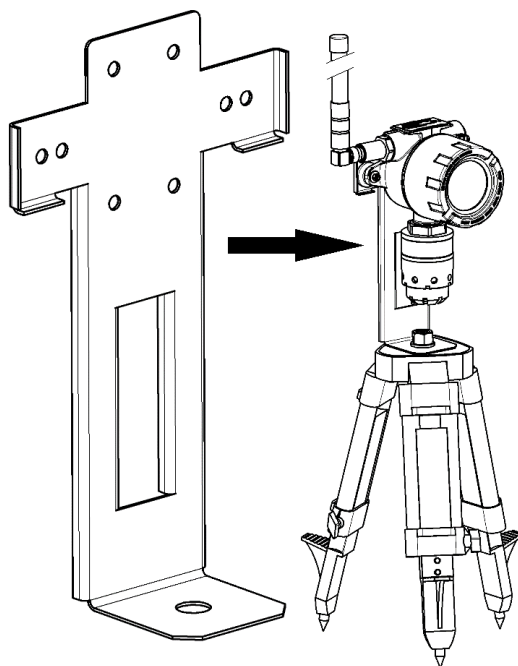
Внешний вид газоанализатора на штативе геодезическом и крепежная пластина для крепления ДГС
